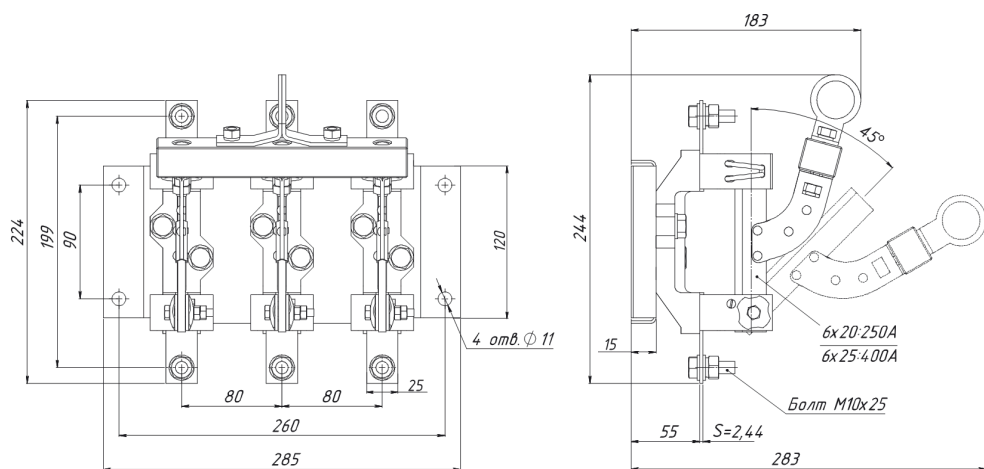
Разъединитель РЕ19-35(37)-31170-00 УХЛЗ с рукояткой для полюсного оперирования
